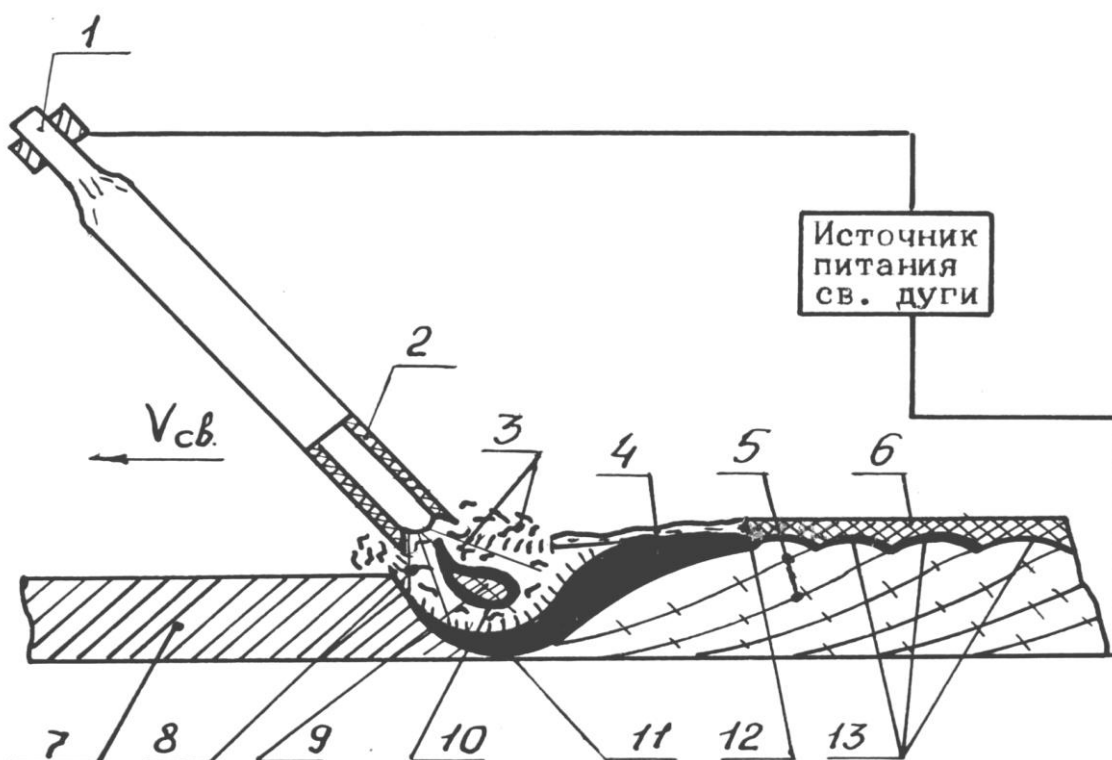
Схема плавления электрода и образования сварного шва:
